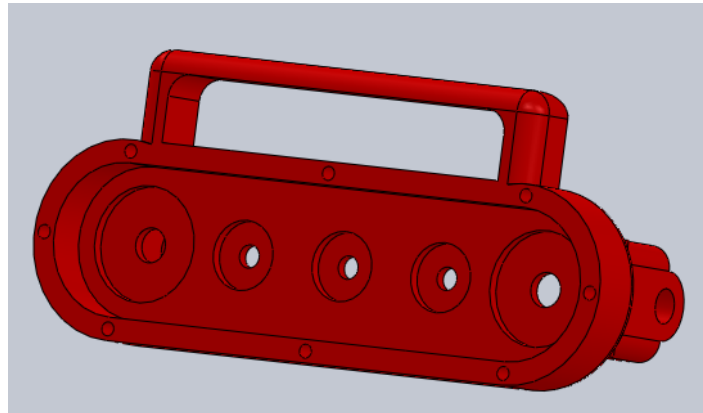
Cortes circulares en el interior de la carcasa del sistema de engranajes.
